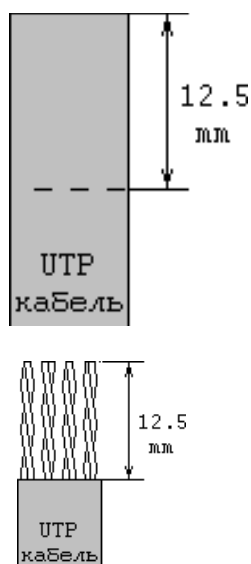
Зачистка оболочки витопарного кабеля
